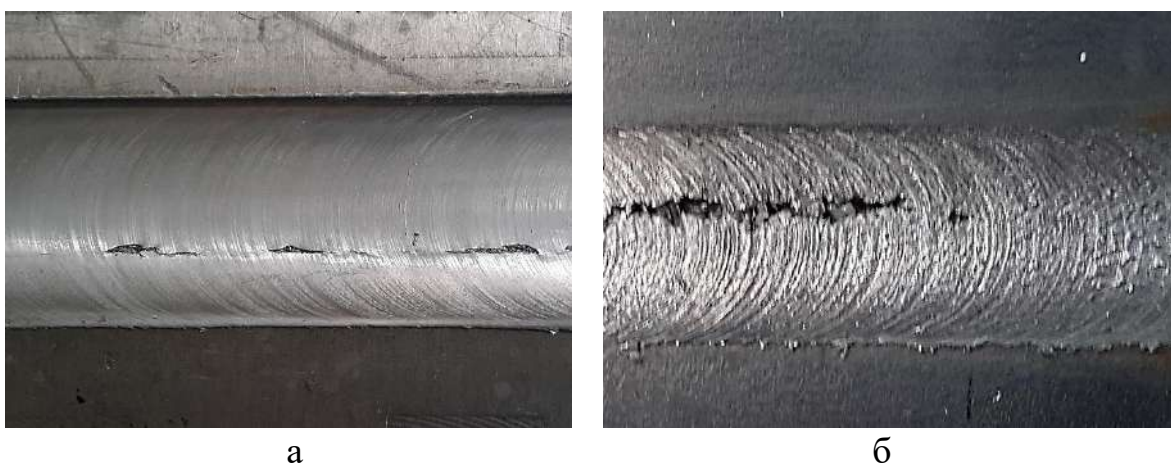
Непротяженные несплавления в сварных швах алюминиевых сплавов при сварке трением с перемешиванием
